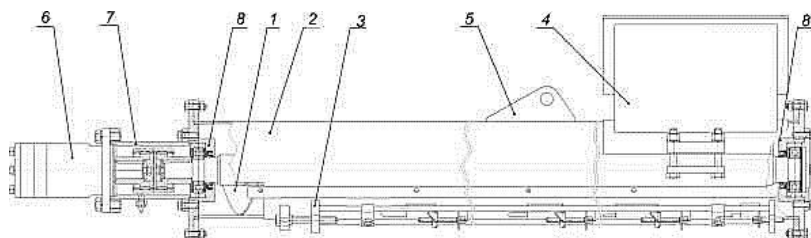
Штанга: *1* – шнек; *2* – кожух; *3* – регулировочное устройство; *4* – загрузочная горловина; *5* – зацеп; *6* – гидромотор; *7* – муфта; *8* – подшипниковый узел
